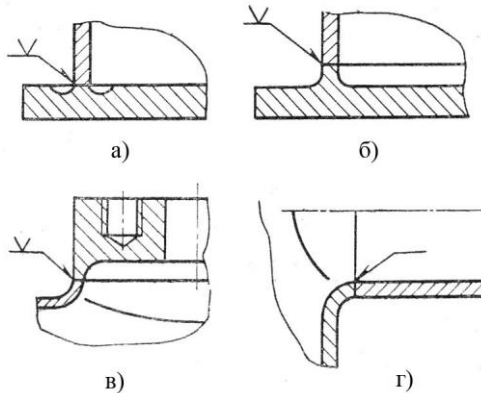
Конструктивное оформление сварных узлов деталей из высоколегированных сталей созданием равнотолщинности: а) обечайка и трубная решётка с проточками; б) обечайка и трубная решётка с выступом; в) обечайка и бобышка; г) обечайка и патрубок фланца
